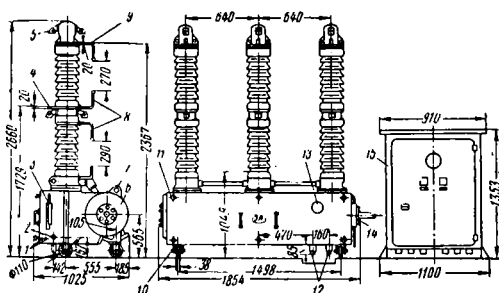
Выключатель типа МКП-35: 1—указатель уровня масла; 2—указатель положения; 3—привод ШПС-30; 4—рычажок ручного отключения; 5—болт заземления; 6—газоотвод и аварийный клапан; 7—маслоспускной кран; 8—табличка с данными выключателя и трансформаторов тока; 9—лебедка с рукояткой; 10—заводской щиток; 11—кабельные муфты
